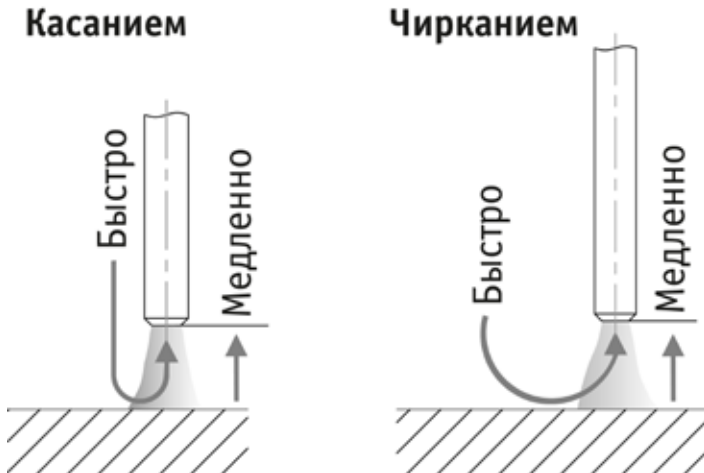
Способы зажигания сварочной дуги.
